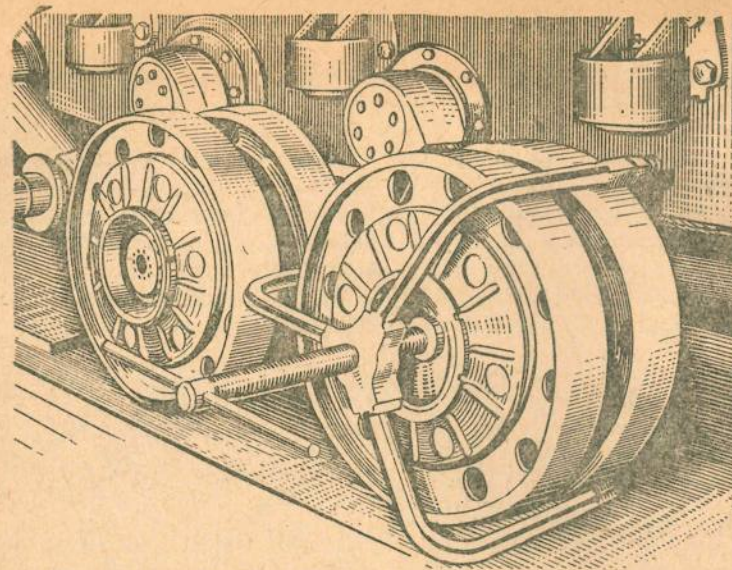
Снятие нижнего катка с оси балансира при помощи приспособления
